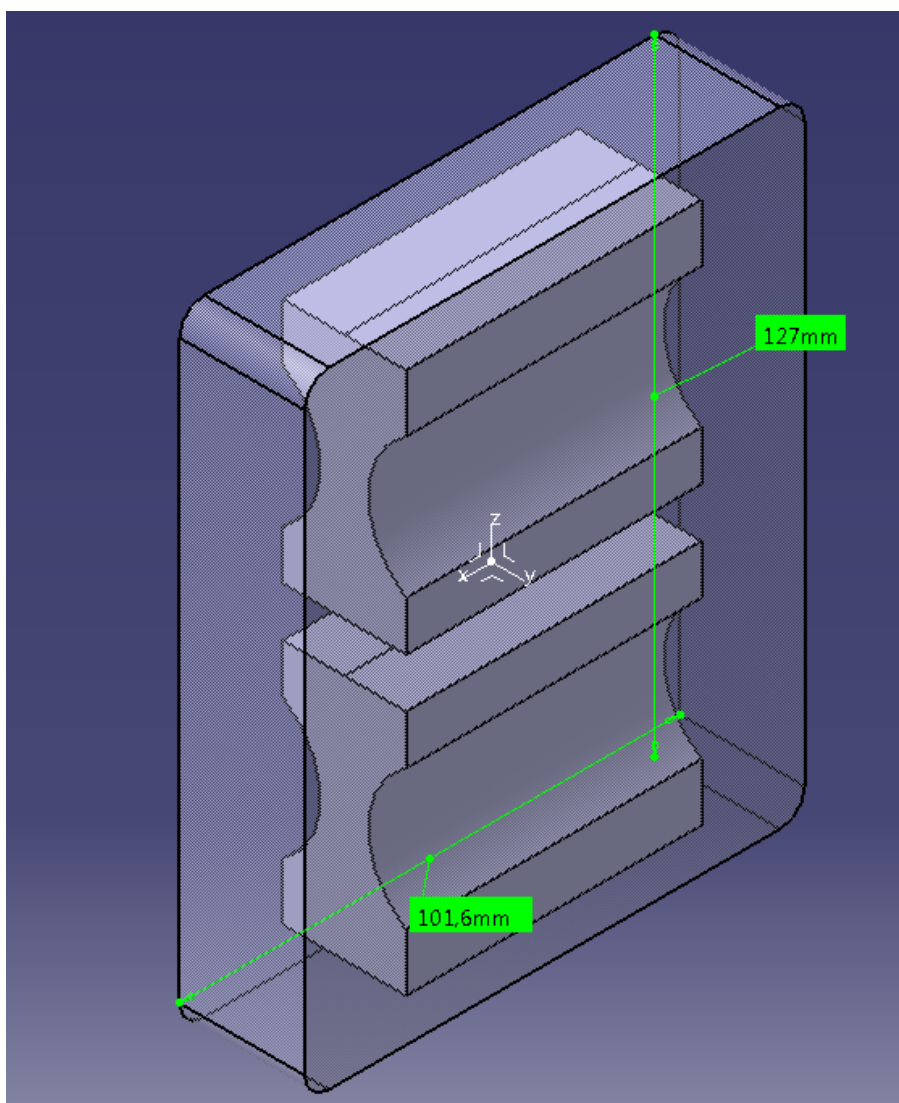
Usinage des éprouvettes dans une plaque d'alliage coulée
